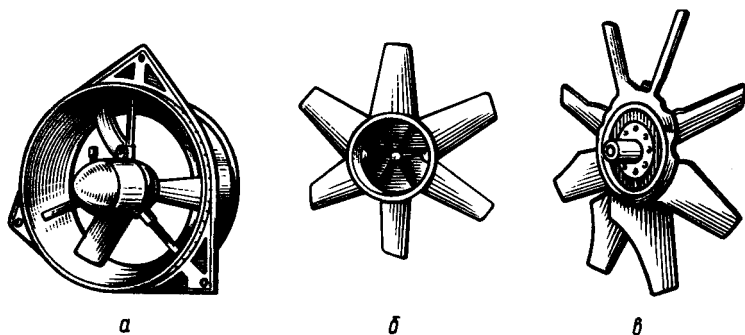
Осьовий вентилятор (а) та конструкція осьового зварного лопаточного (б) і штампованого колеса (в)
